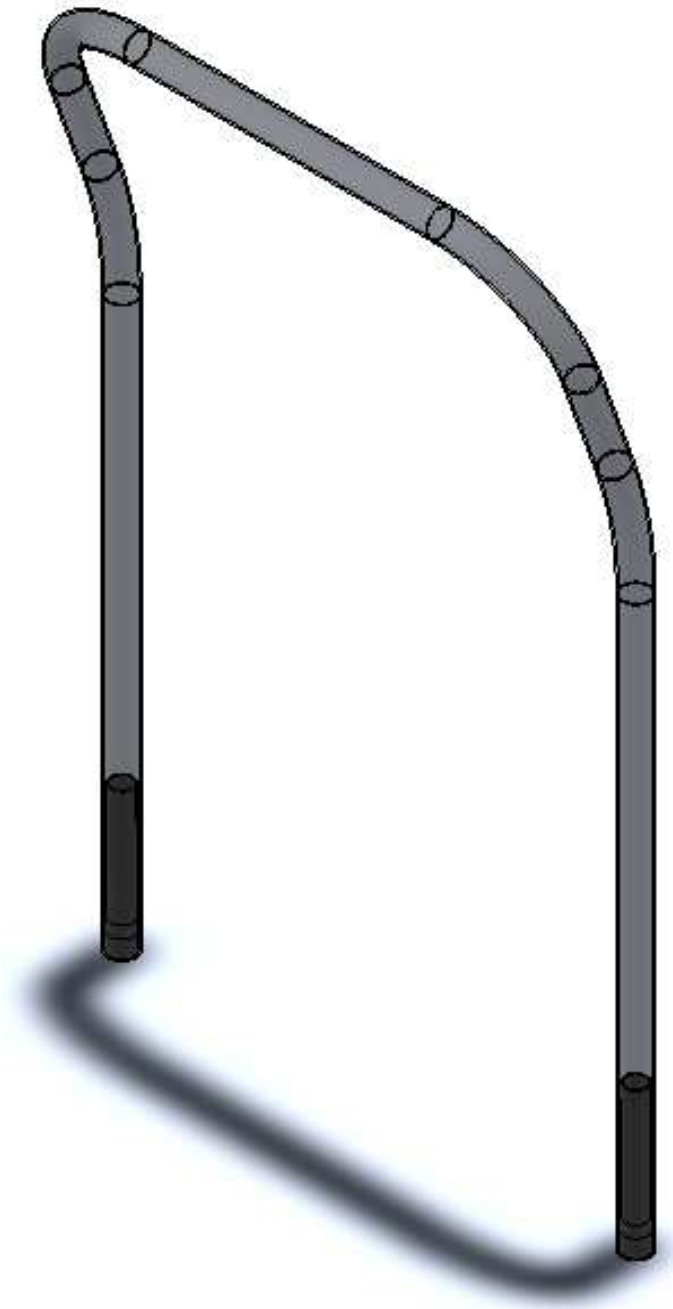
Detalle ensamblaje tubo bastidor-tubo refuerzo
